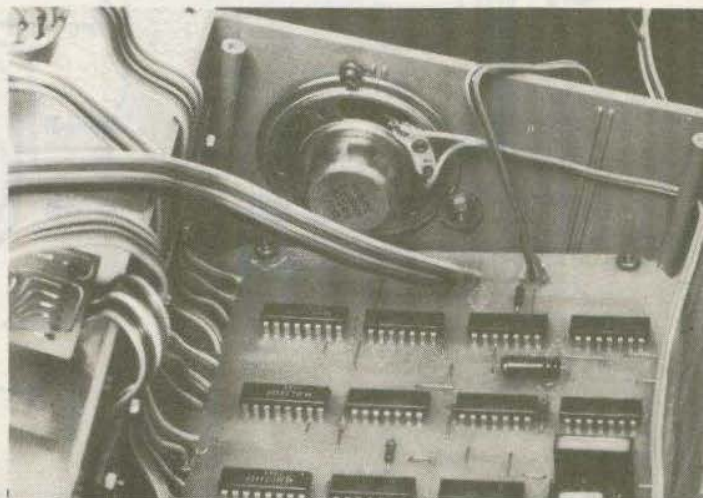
On disposera le petit haut-parleur 8 Ω sur une face latérale du boîtier.
